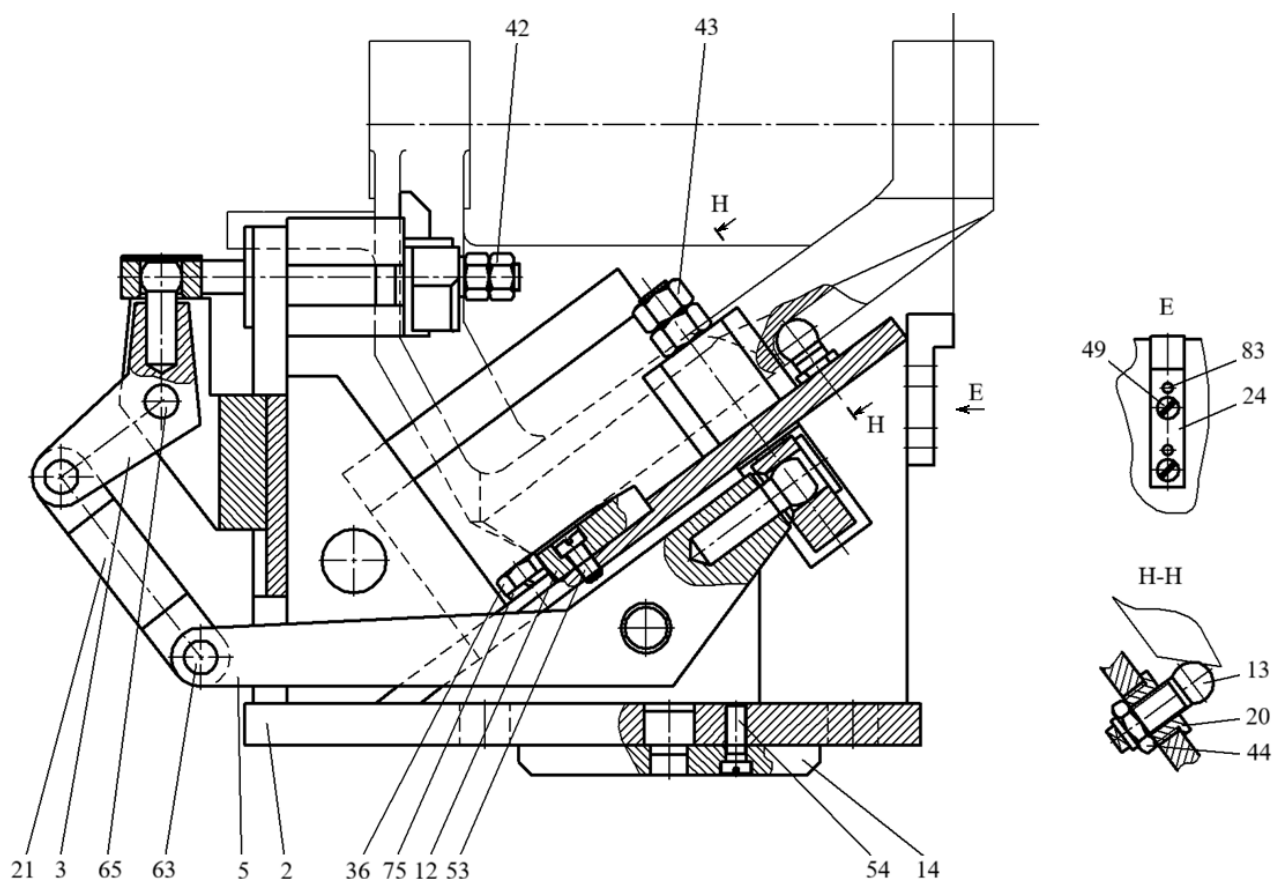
Пристрій для фрезерування бічних площин
